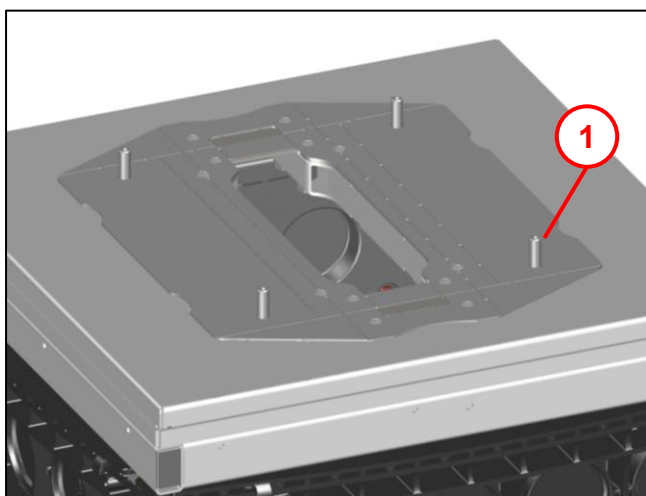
a Obr. 24 dodržujte pouze u varianty Alpitronic® HYC1000 Dispenser MCS:
